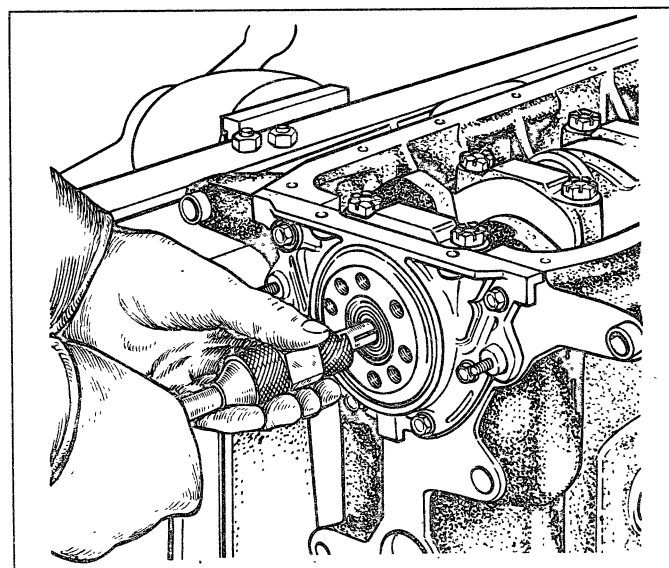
Выпрессовывание подшипника вала коробки передач из коленчатого вала выталкивателем А.40006
